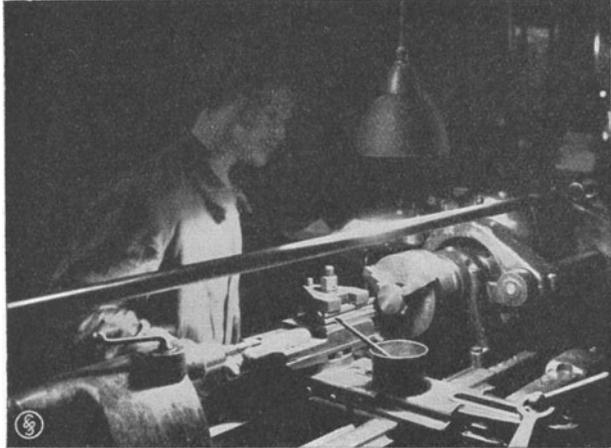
Zweckmäßige Werkbankbeleuchtung, Lampe abgeschirmt, Werkstück gut beleuchtet.
